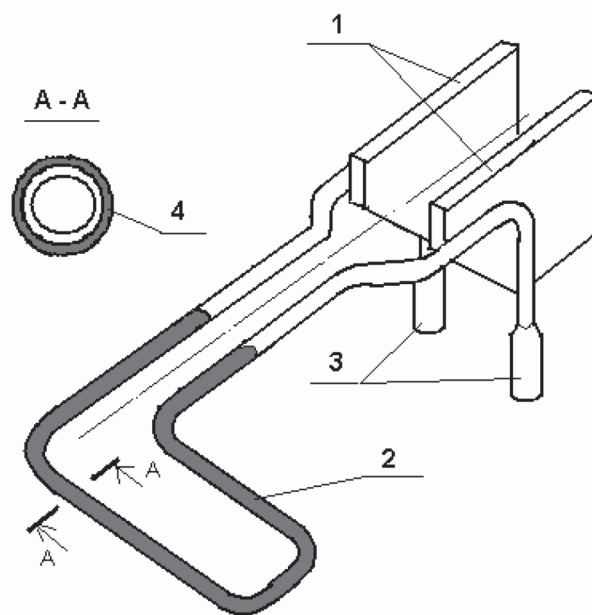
Индуктор для напайки резцов: 1 – шины-колодки; 2 – индукционный виток; 3 – штуцера; 4 – система изоляции витка
